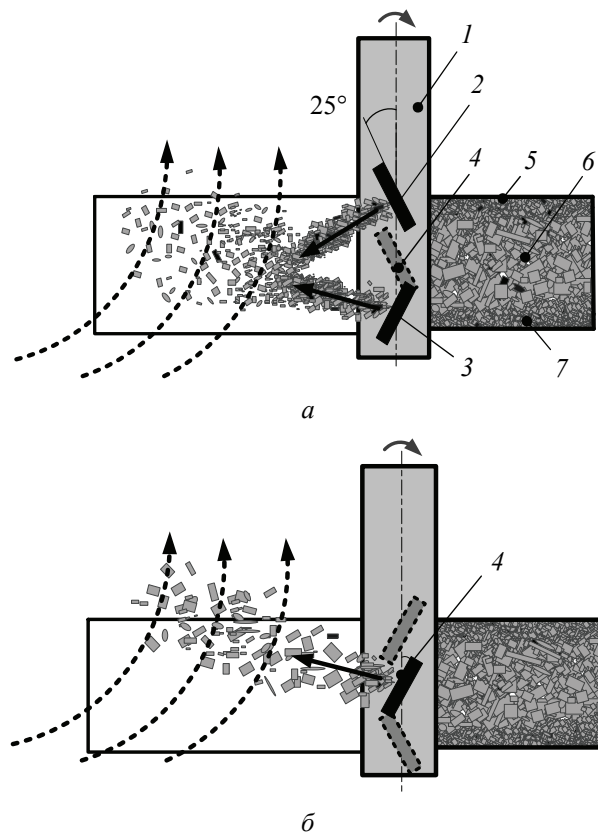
Схема обработки древесного материала хвостовой фрезой в процессе работы пары (а) и отдельного (б) режущих элементов
